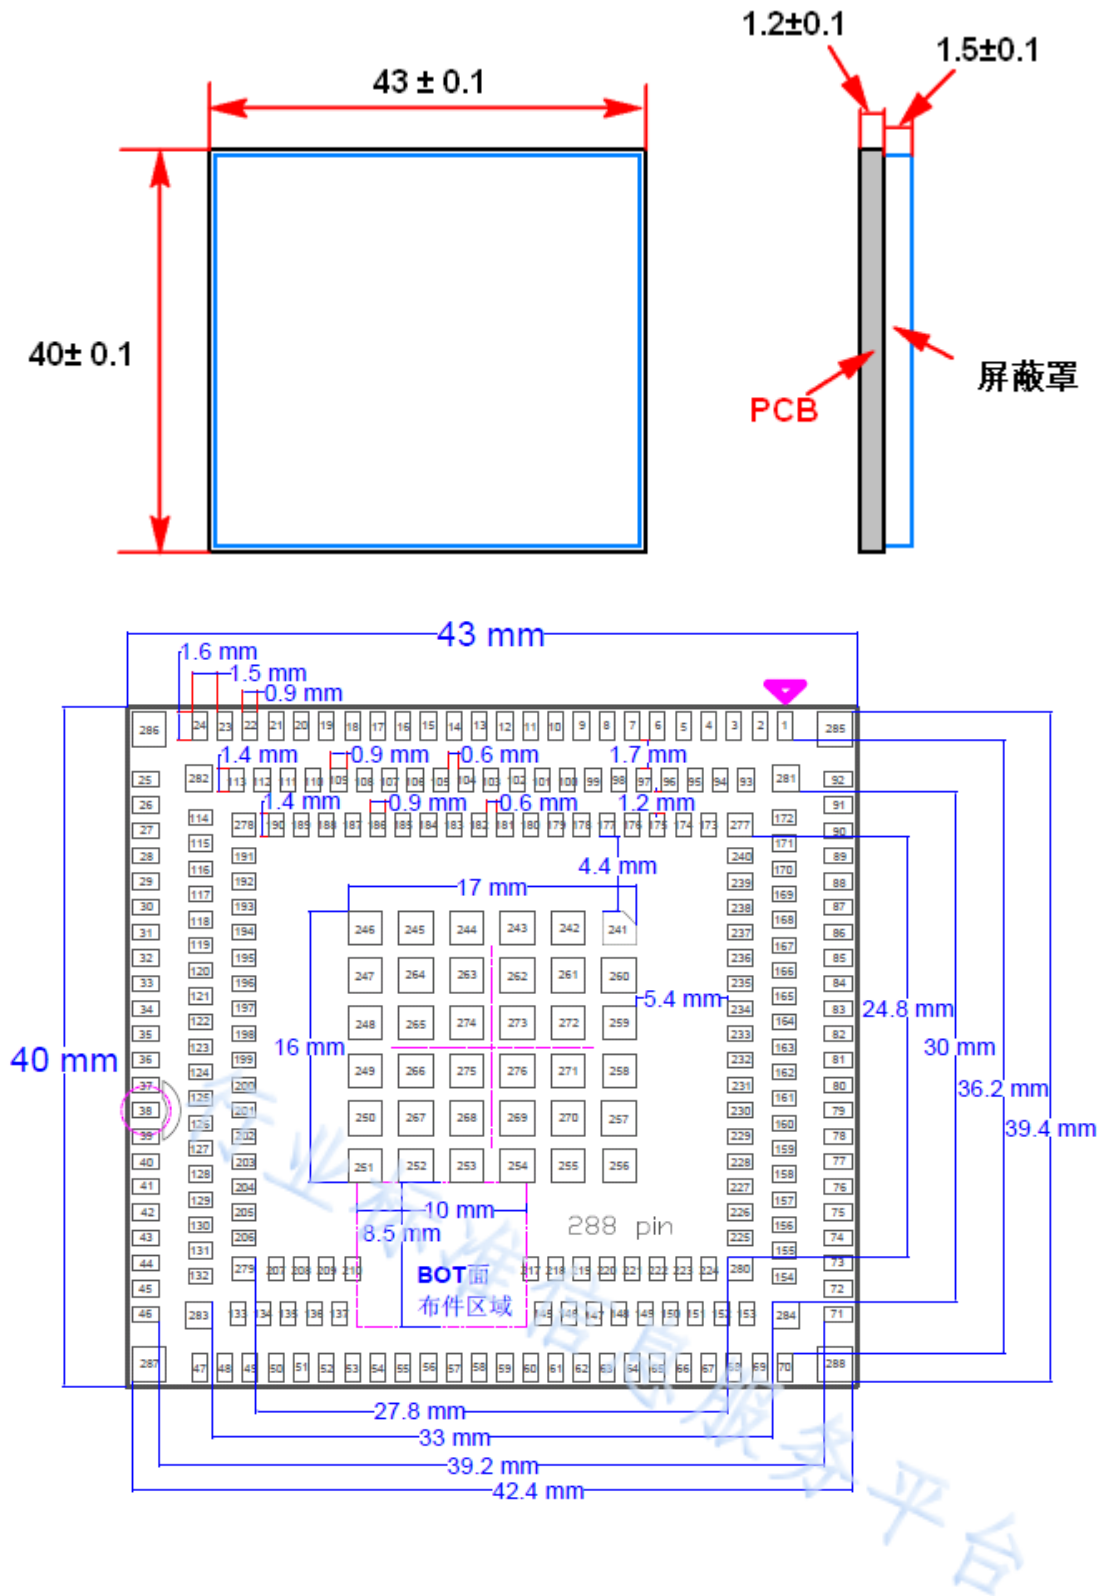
SLB4242封装尺寸、焊盘尺寸和布局（单位：mm）
